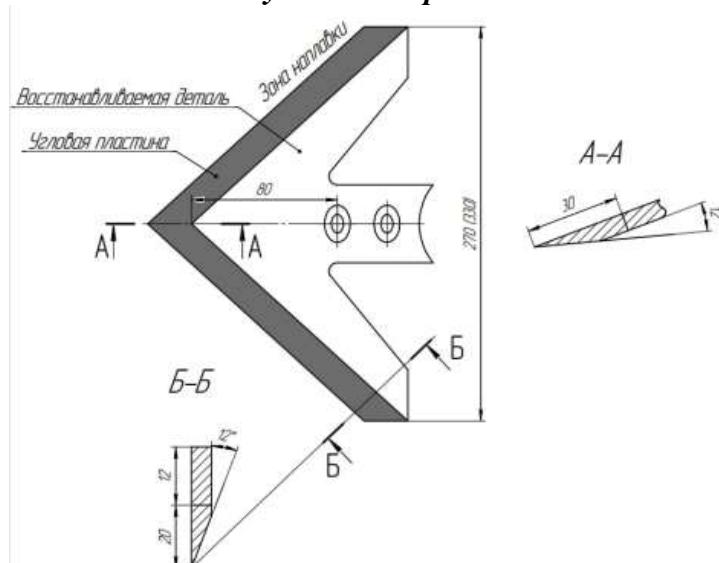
Схема восстановления стрельчатой лапы культиватора
